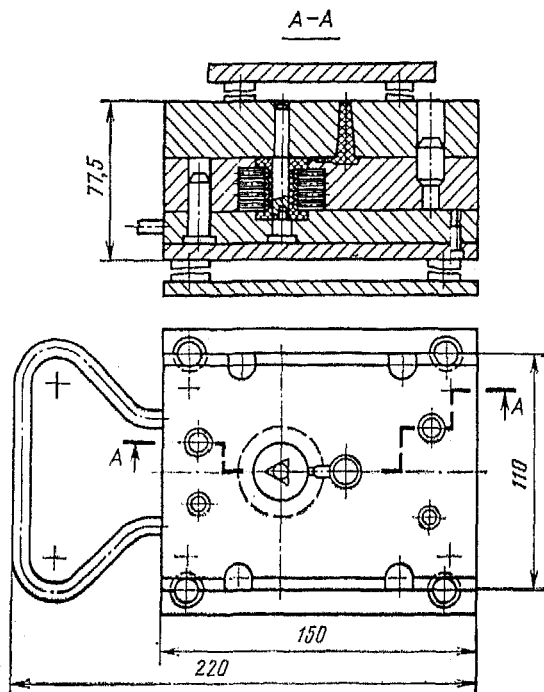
Литьевая пресс-форма для заливки корпуса щетки
